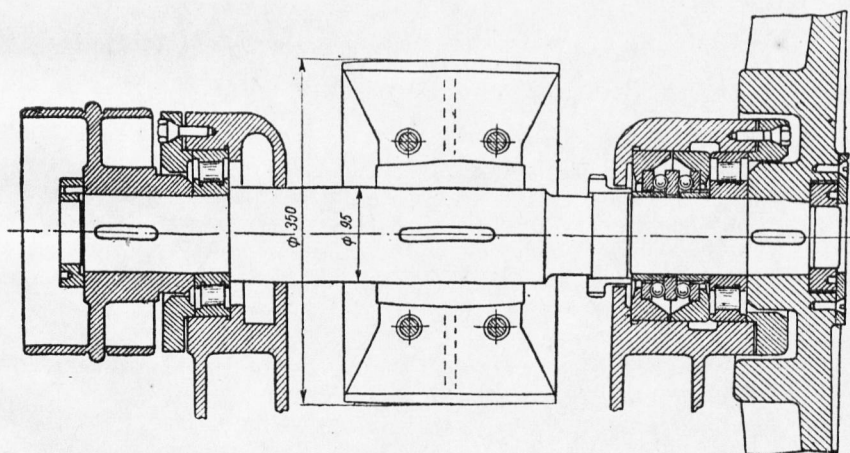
Конструкция шпинделя шлифовального станка „Дискус“
